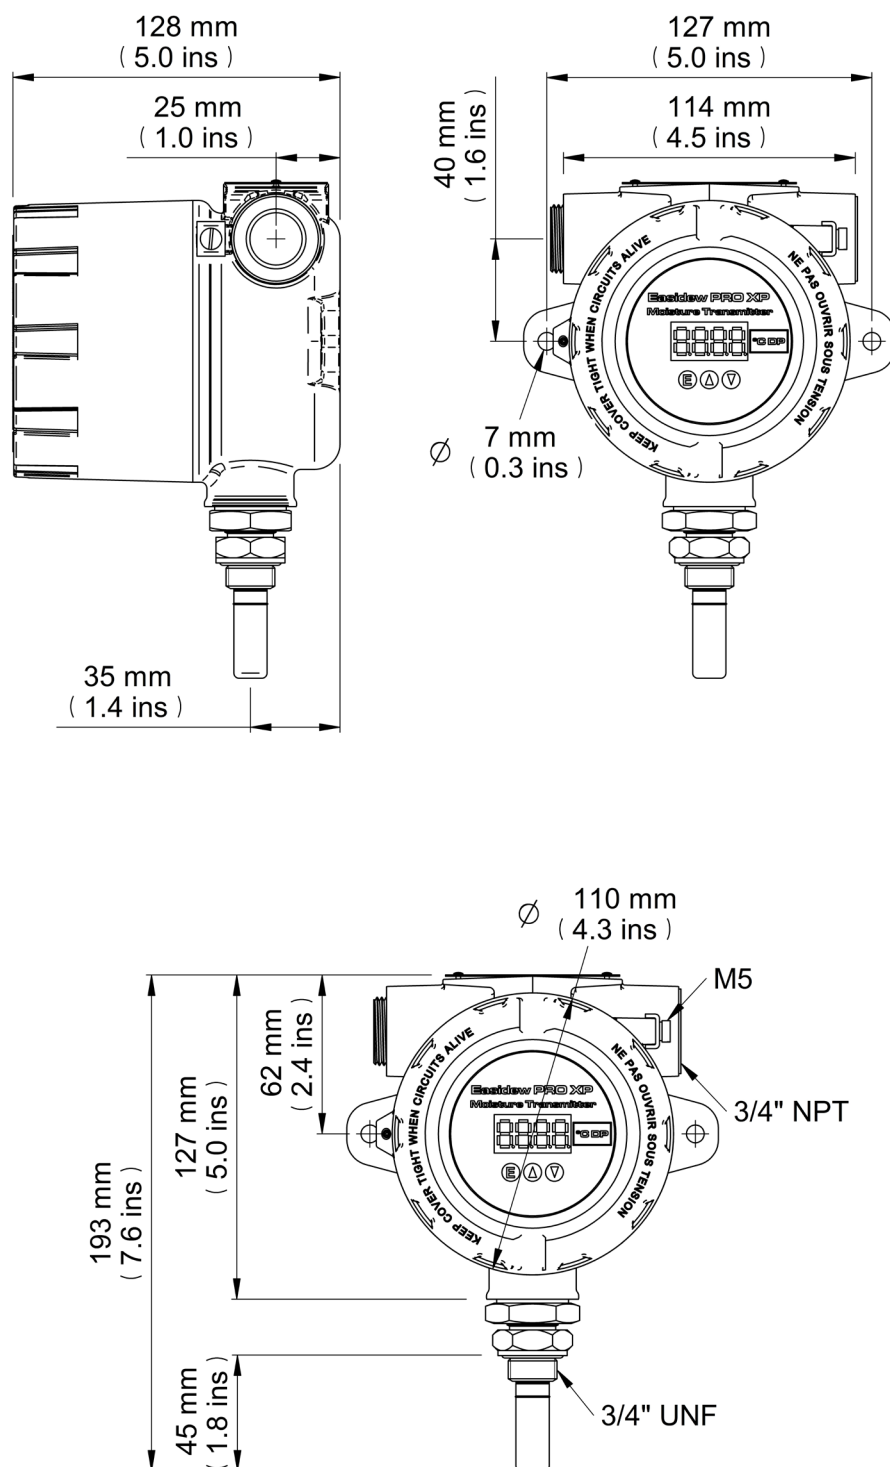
Esboço das dimensões PRO XP EX2 (Com Display) - Montagem em parede
